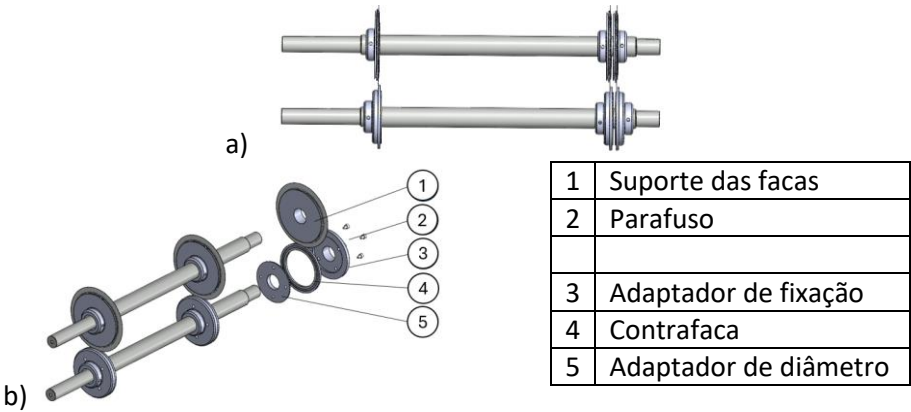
Solução 4: a) vista frontal; b) vista explodida.
